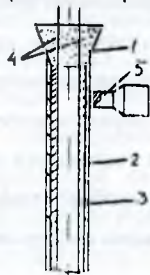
Схема засыпки порошка с помощью УЗК: 1 - воронка; 2 - направляющая; 3 - груба - заготовка; 4 - порошок; 5 - преобразователь УЗК.
